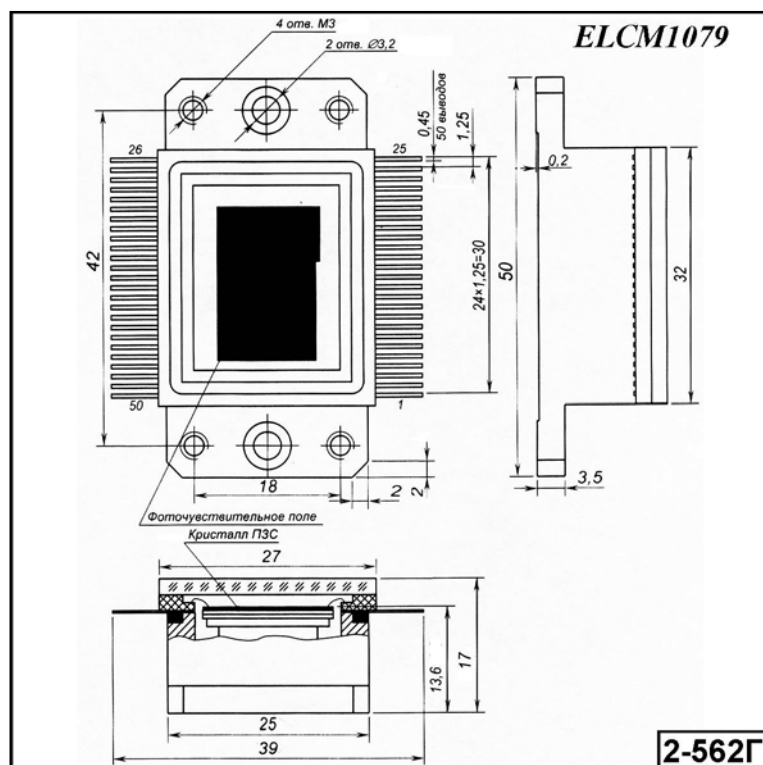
Внешний вид и габаритные размеры ФПЗС ELCM1079
